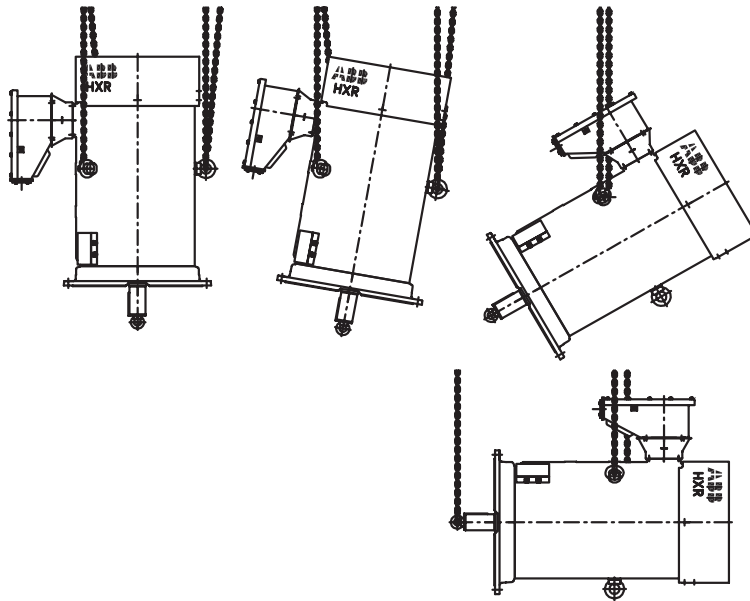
Машина с поворачивающимися рымами: подъем и поворот
